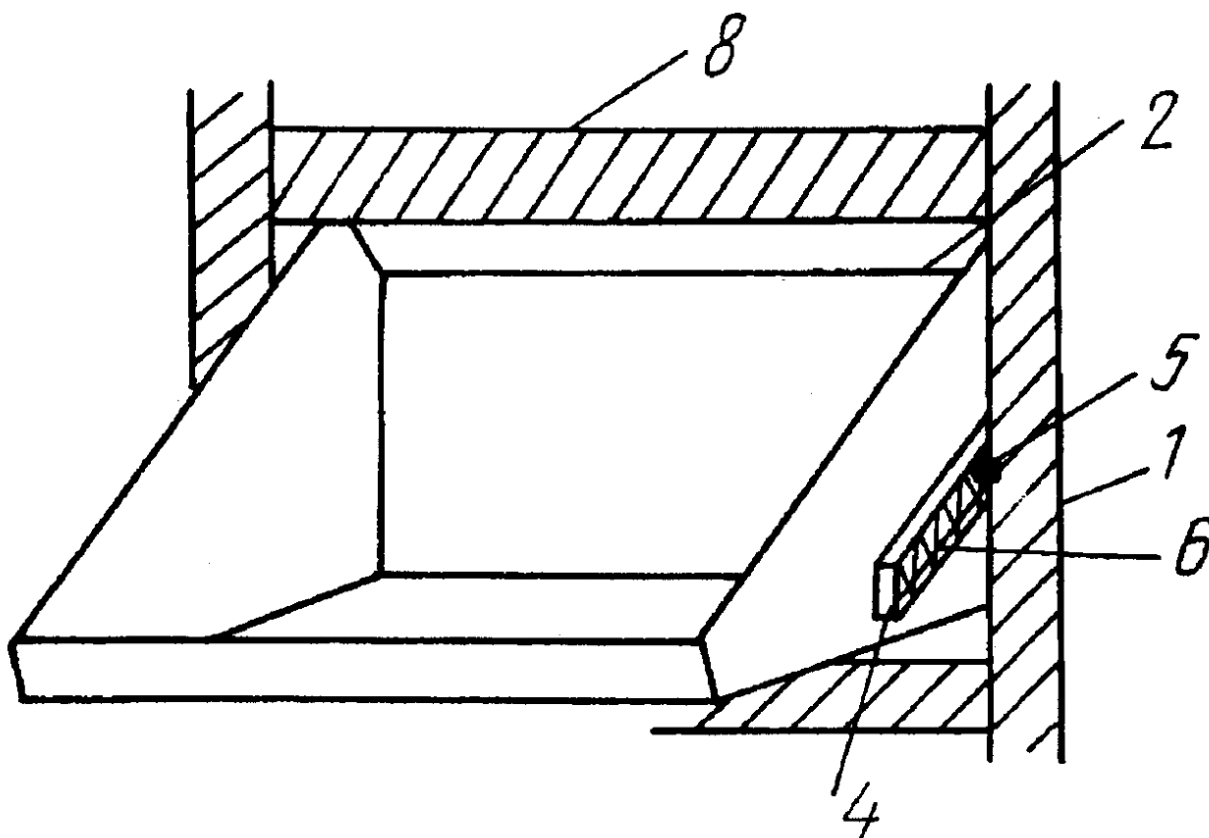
Кормушка в загрузочном положении: 1 – корпус; 2 – лоток; 3 – фиксатор; 4 – направляющие пазы с приспособлением для поворота; 5 – оси; 6 – пружины; 7 – толкатели; 8 – перекладина корпуса.
